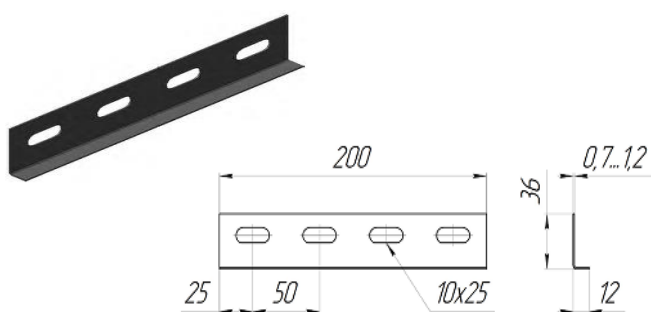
Соединитель лотка лестничного универсальный с бортом 50-65 (1,2) ПожТехКабель
